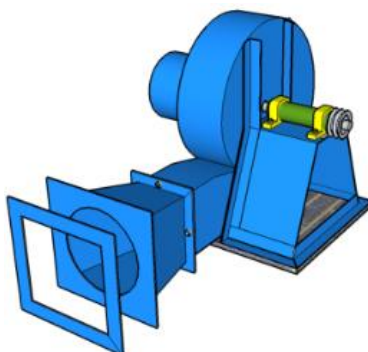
Ventilador centrífugo com rotor de oito pás e 35 cm de diâmetro.
